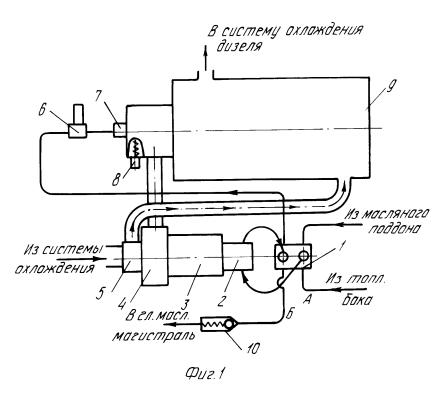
Устройство для предпусковой подготовки ДВС
